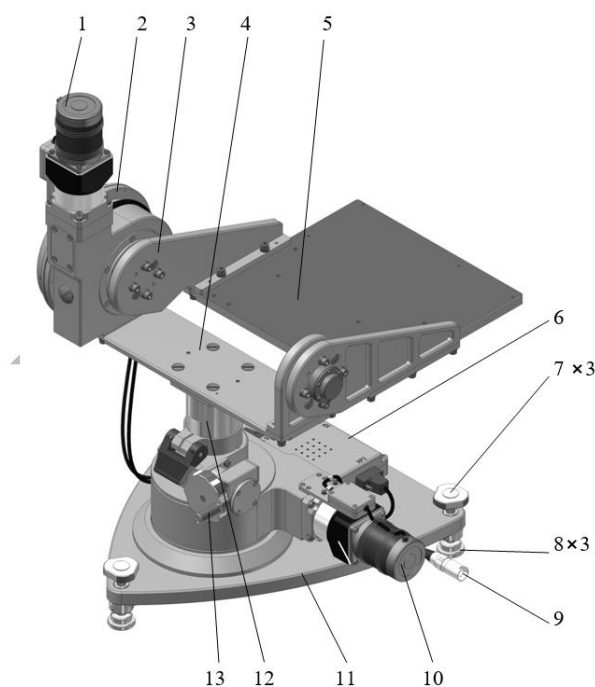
Общий вид стола наклонно-поворотного: 1 – шаговый двигатель; 2 – абсолютный датчик угла поворота; 3 – кронштейн; 4 – плита; 5 – установочная платформа; 6 – блок управления; 7 – винт регулировочный; 8 – опора; 9 – сетевая кабель «+27V»; 10 – шаговый двигатель; 11 – основание; 12 – рейка; 13 – ручка
